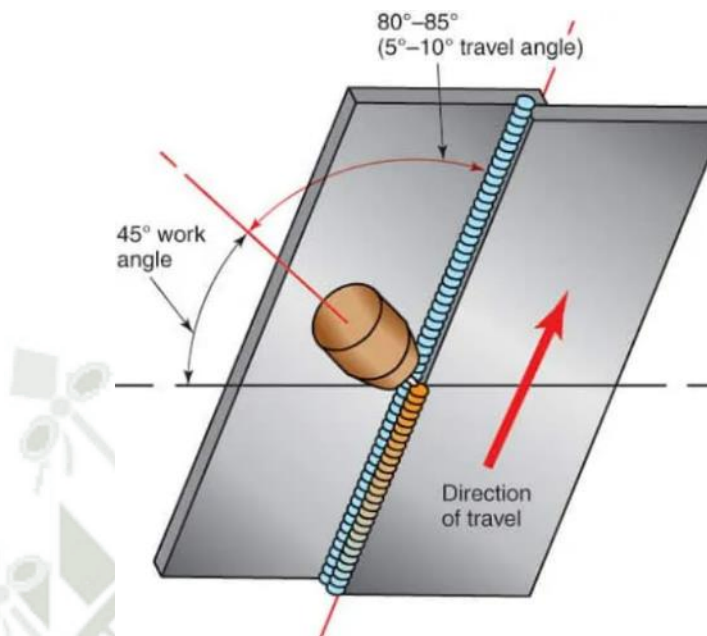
Representación de la soldadura tipo filete por posición de cabeza.
